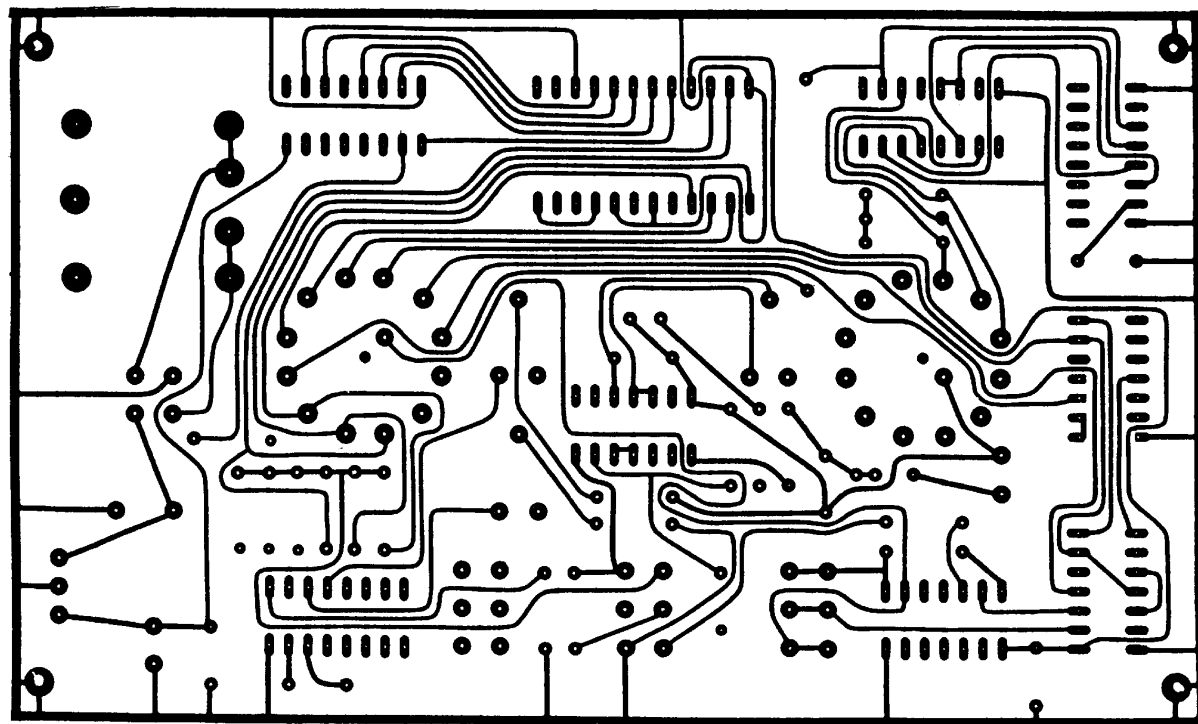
De soldeerzijde van de dubbelzijdige print.
